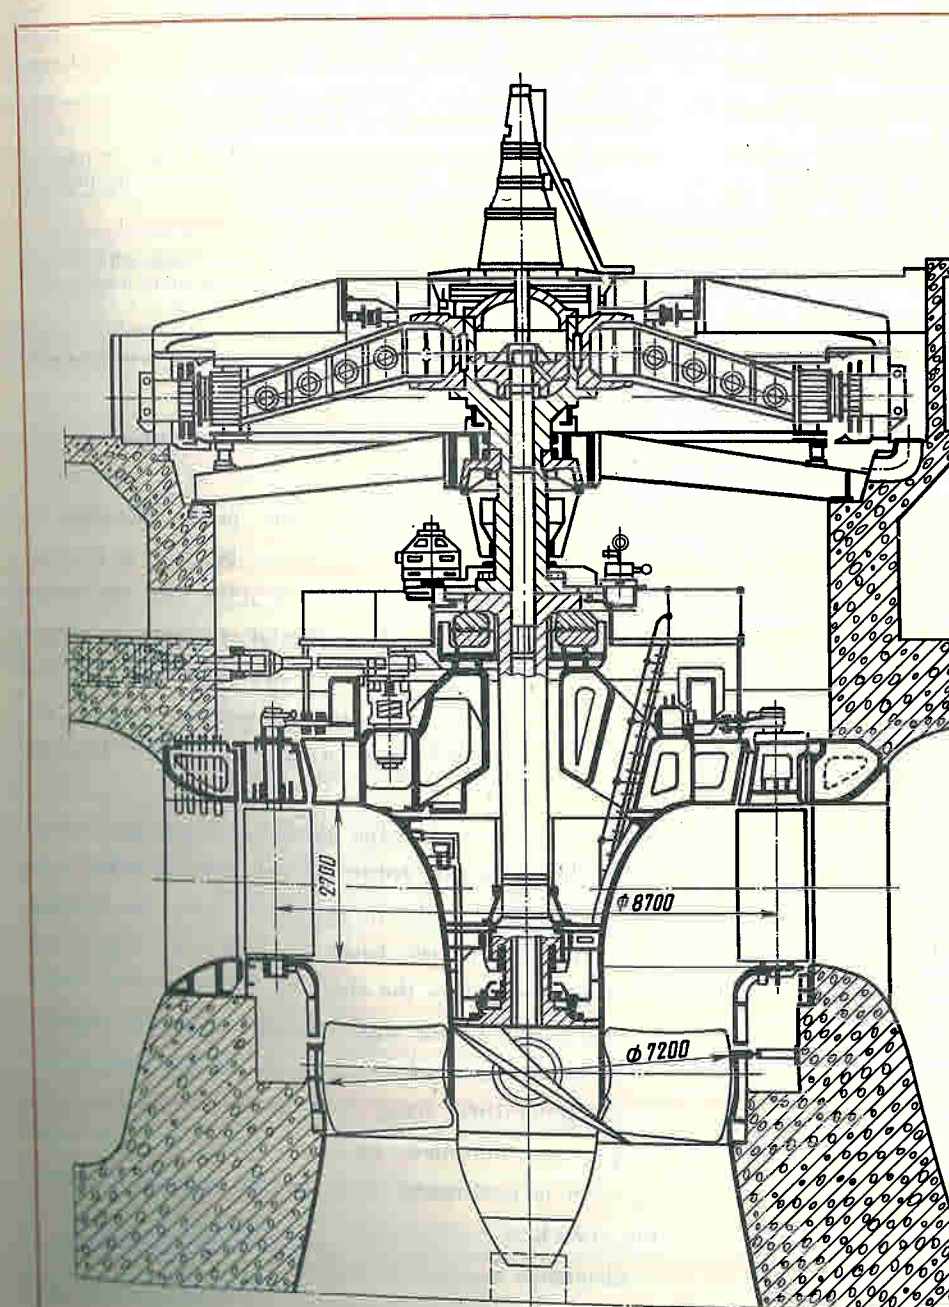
Вертикальный гидроагрегат с расположением сервомотора рабочего колеса во втулке ротора и подпятником на крышке турбины
